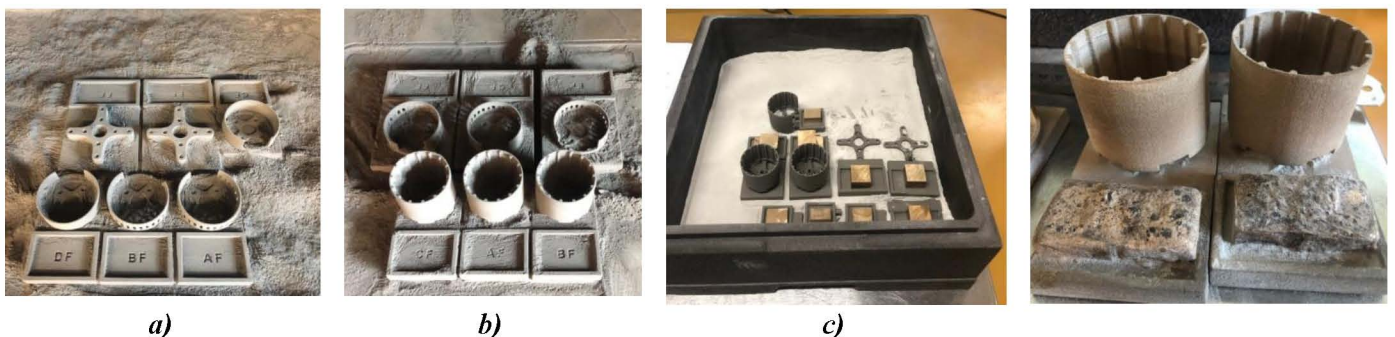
Fabricarea aditivă a componentelor motorului electric utilizând procedeul SLS: a) carcasă stânga și flanșă de prindere; b) rotor; c) pregătirea componentelor pentru infiltrare în cuptorul de sinterizare; d) componentele obținute după infiltrare
